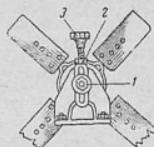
Регулиро- вка натяжения ремня вентиля- тора ЗИС-5
